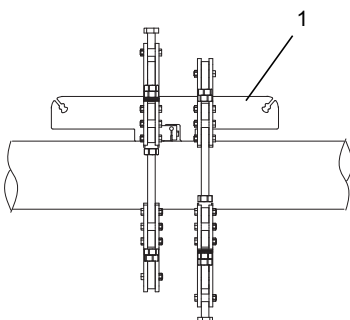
Dispositifs de fixation montés sur la conduite (montage diagonal, vue de côté)
